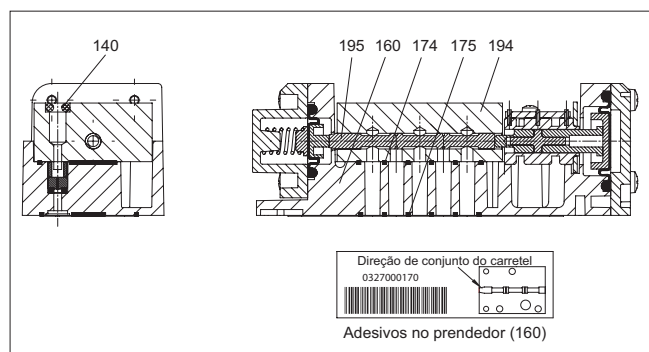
Conjunto da válvula de carretel, ND9100 e ND7100
